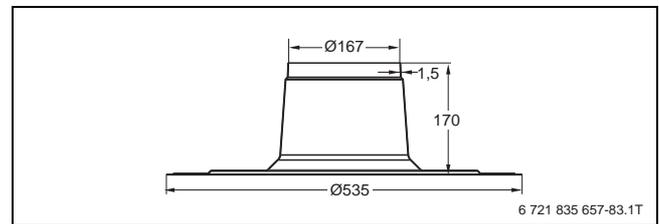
Flachdach-Klebeflansch (Maße in mm)
